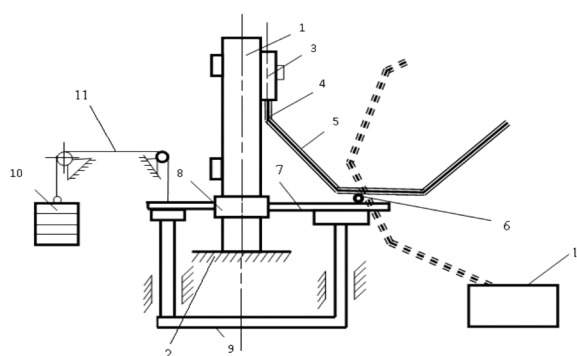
Устройство для загрузки камеры шерстопресса: 1 – стойки; 2 – рама прессы; 3 – направляющие; 4 – втулки; 5 – клиновидное ложе; 6 – ось; 7 – подставка; 8 – ошейники; 9 – рамка; 10 – груз; 11 – троссоблочный механизм; 12 – камера шерстопресса
